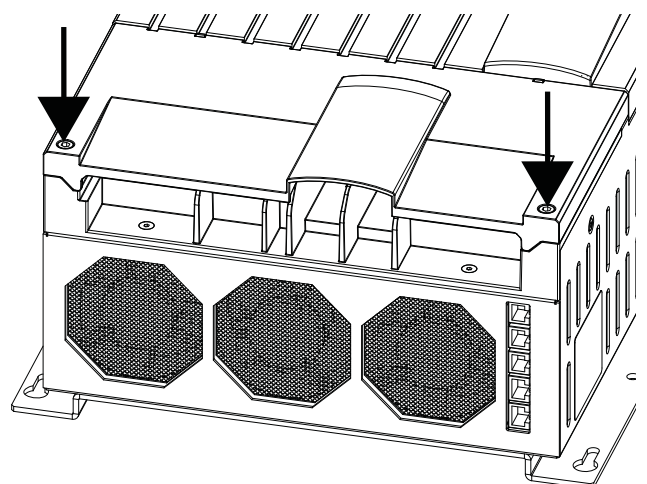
Ouverture du couvercle frontal du boîtier
